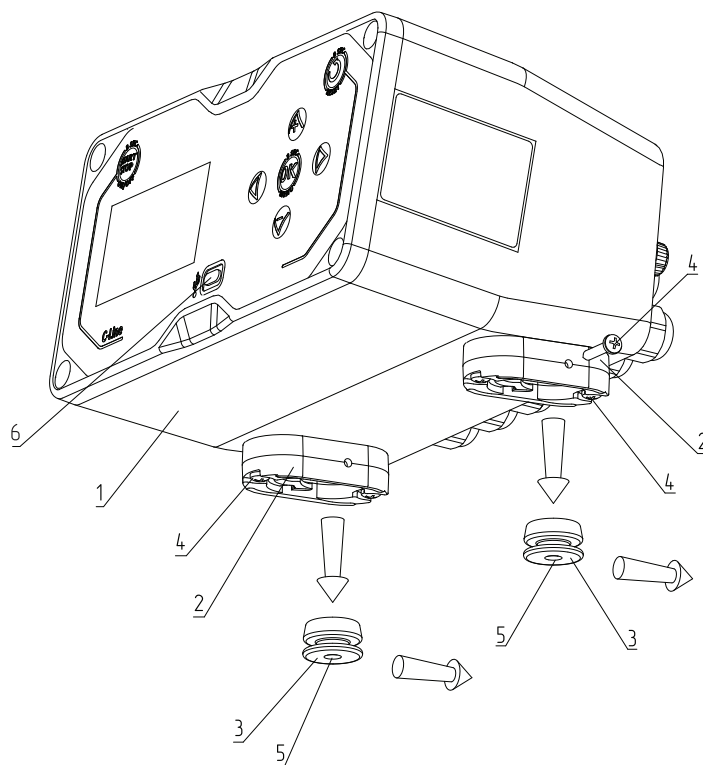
Внешний вид контроллера C-Line 200PA с фиксатором крепления
